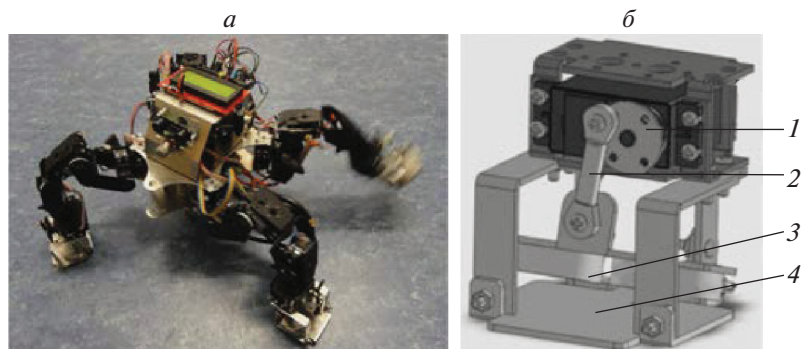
Робот Winspecbot (а), общий вид магнитного фиксатора (б)
